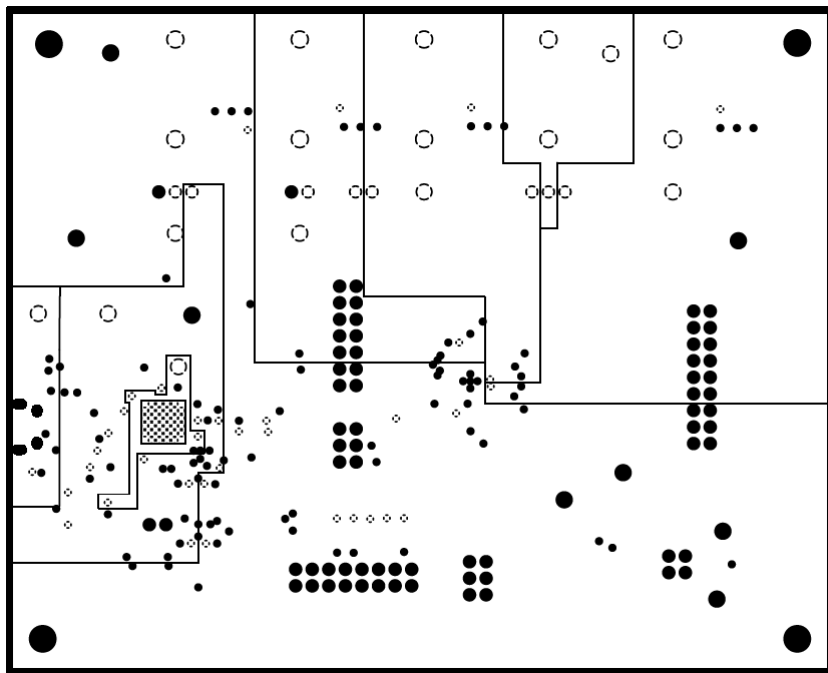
AFE10004EVM PCB 中层 2 布局 (电源平面)
